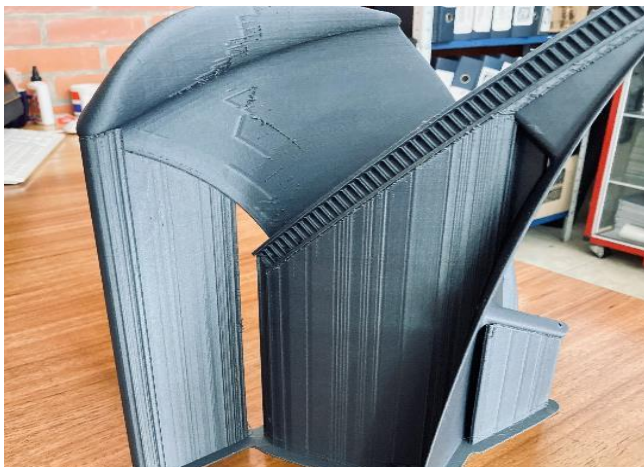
Construcción de aspas de turbina en filamento PLA+Fibra de Carbono.
